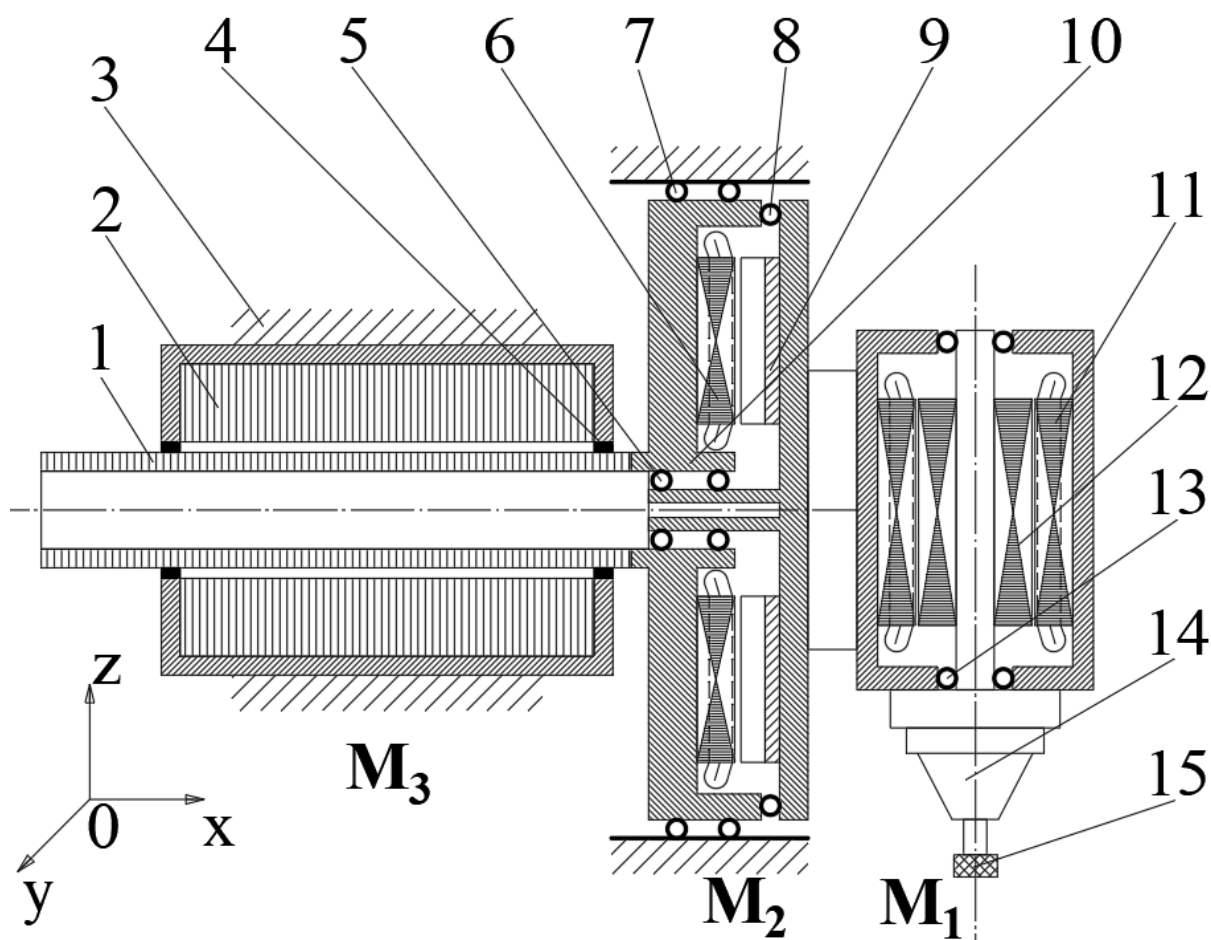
Основні конструктивні вузли розробленої модульної конструкції трикоординатного мотор-шпиндельного агрегату: 1) вторинний елемент двигуна OX подачі; 2) статор двигуна OX подачі; 3) станина верстата; 4) підшипник ковзання; 5) внутрішній кульковий підшипник; 6) магнітопровід статора двигуна кутового положення; 7) ролик опора рухомого статора; 8) упорний підшипник; 9) магнітопровід ротора кутового двигуна; 10) втулка ротора; 11) магнітопровід статора мотор-шпиндель; 12) магнітопровід ротора
